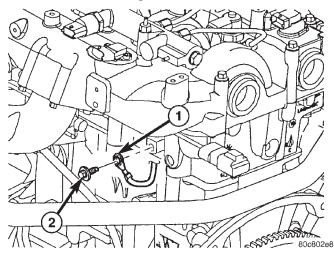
TIRA DE MASA A MOTOR - 2.5L
